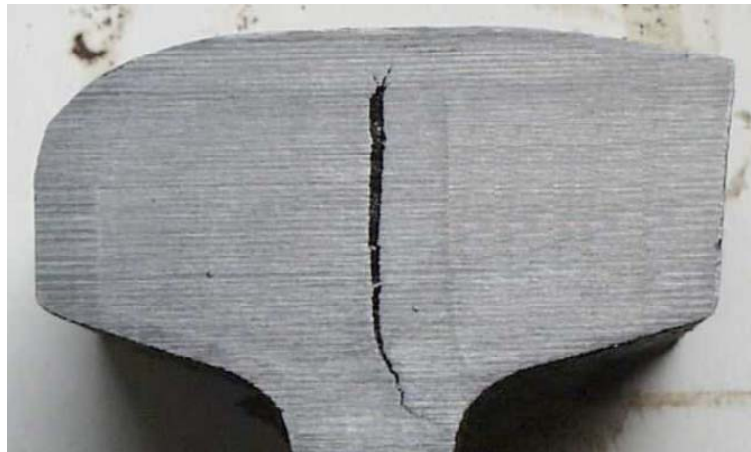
Fisuración vertical de la cabeza
